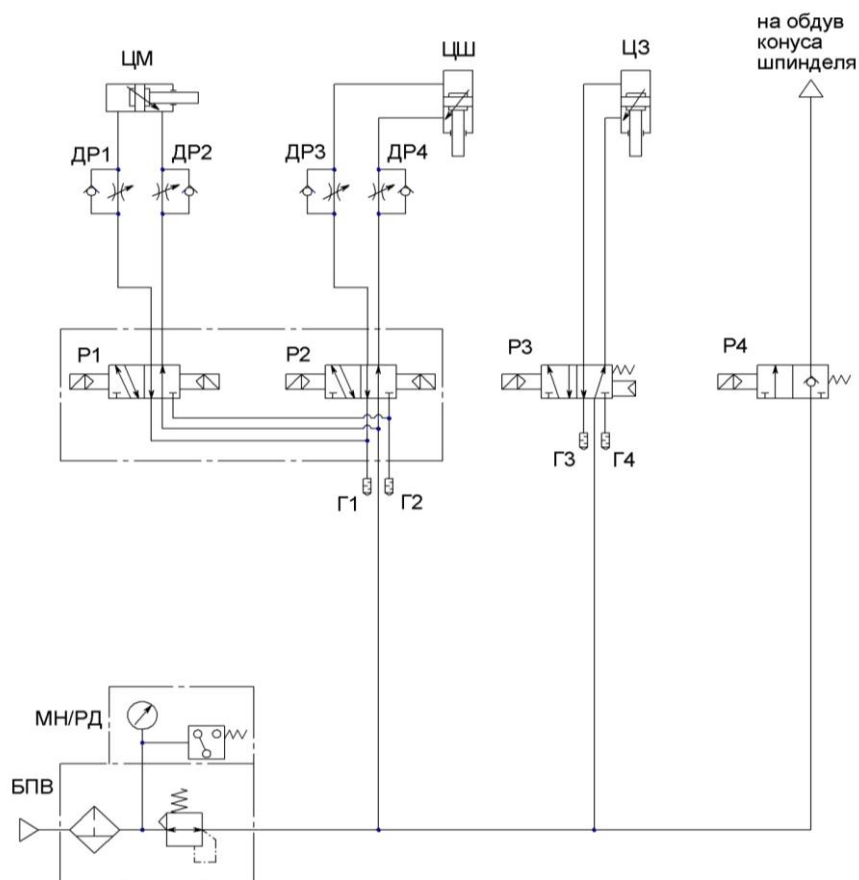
Пневморазводка по станку с линейным инструментальным магазином
